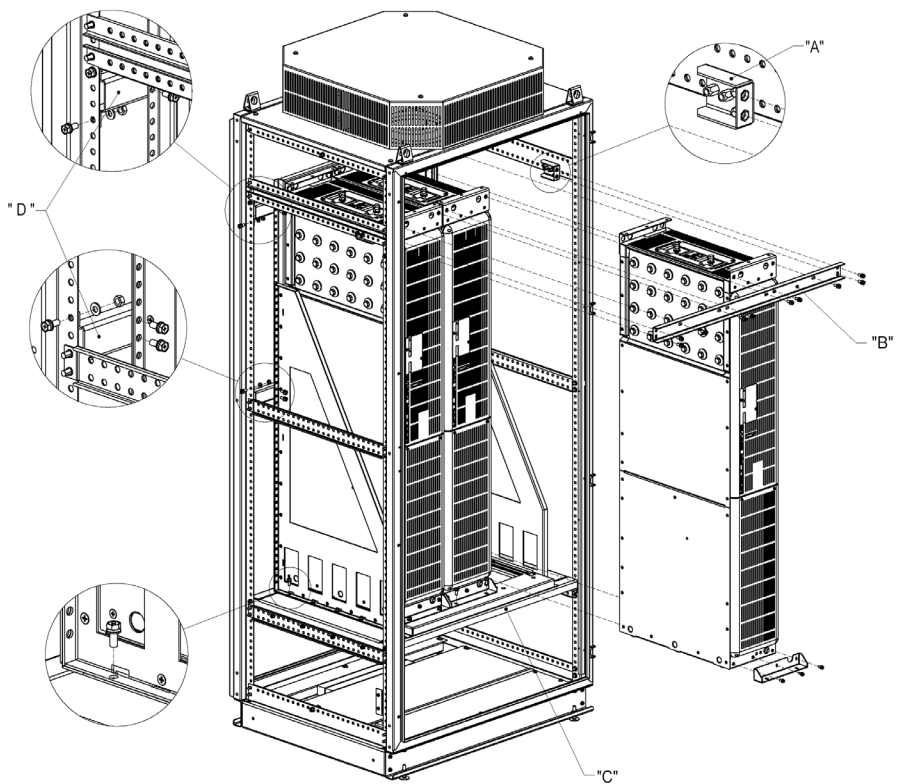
Detalles de montaje del Rack 3 en armario (tablero) con 1000 mm de ancho
